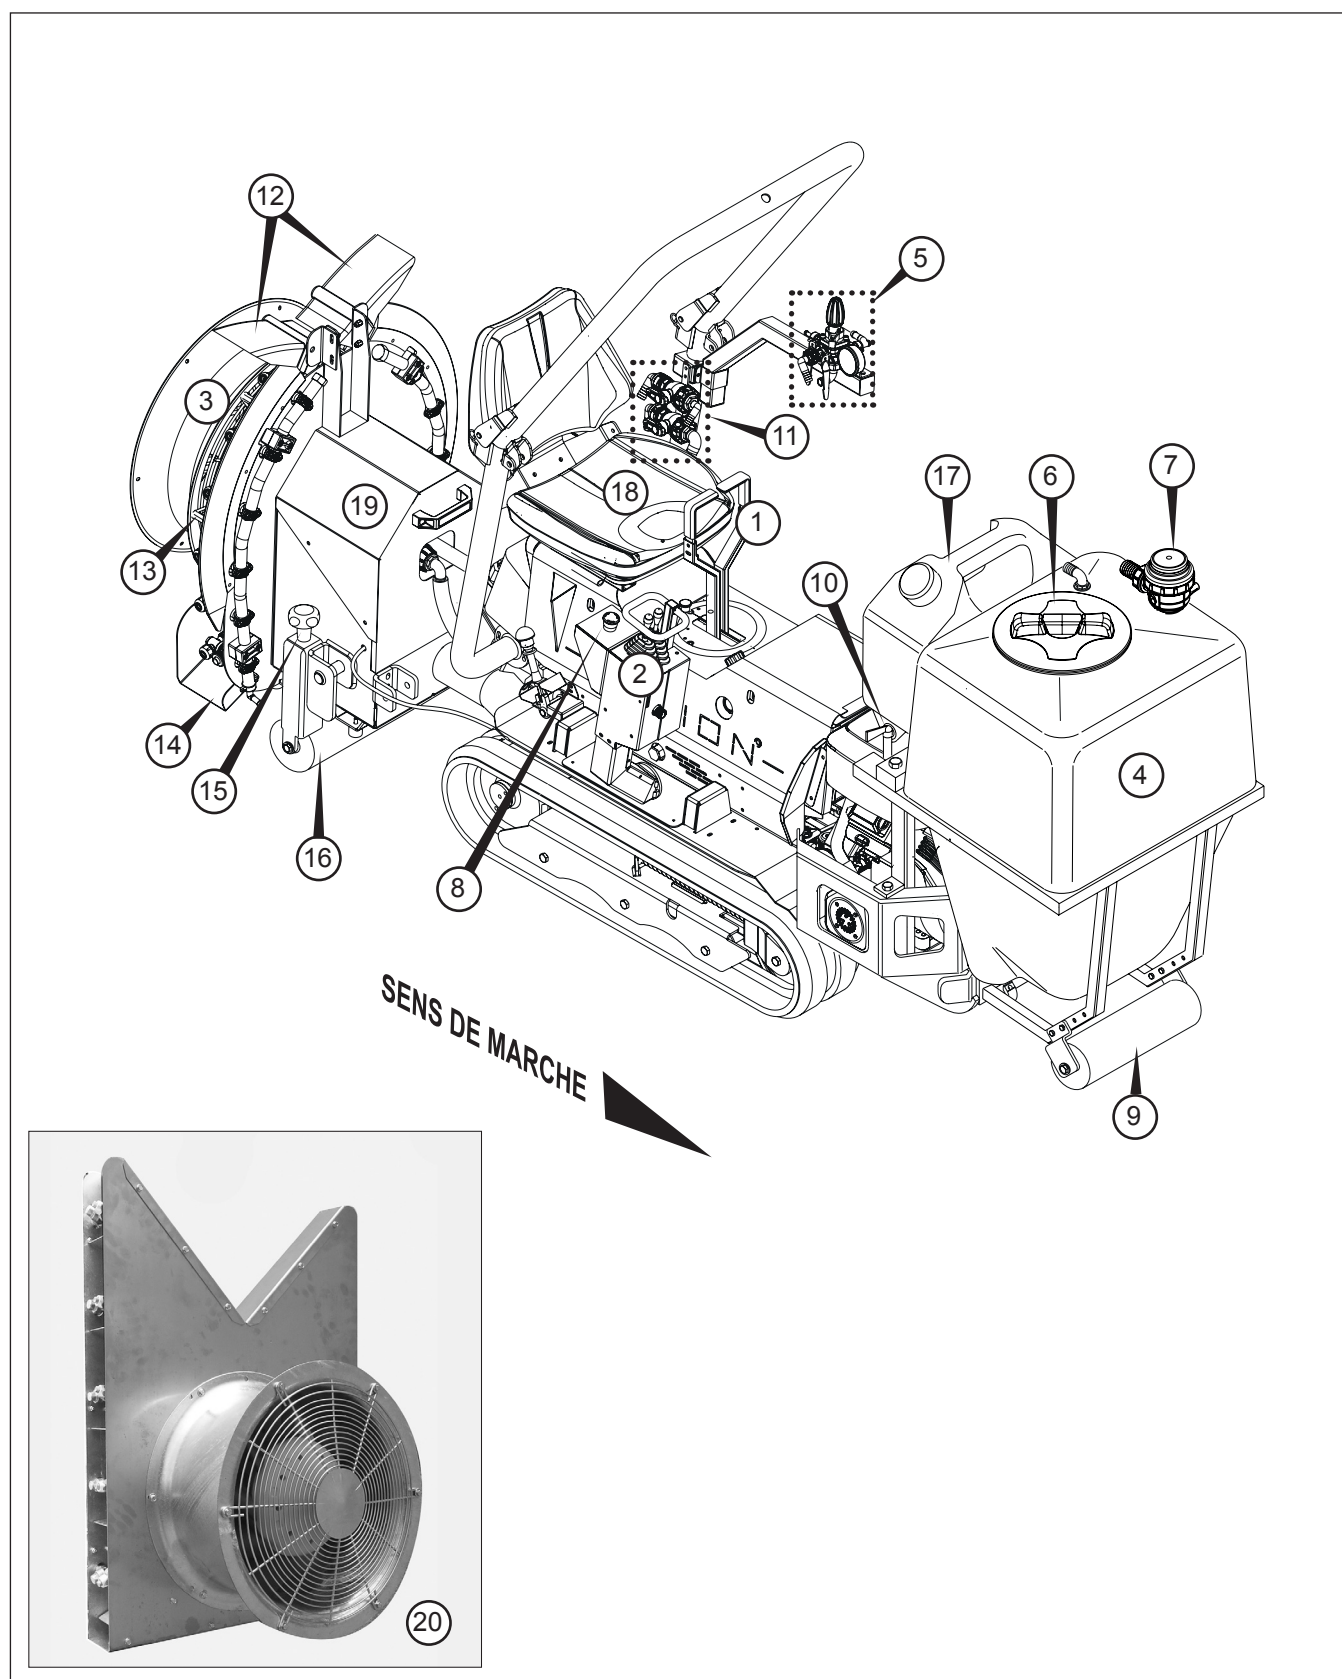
Unité de pulvérisation installée sur la machine multifonctions Vision - Principaux composants.
